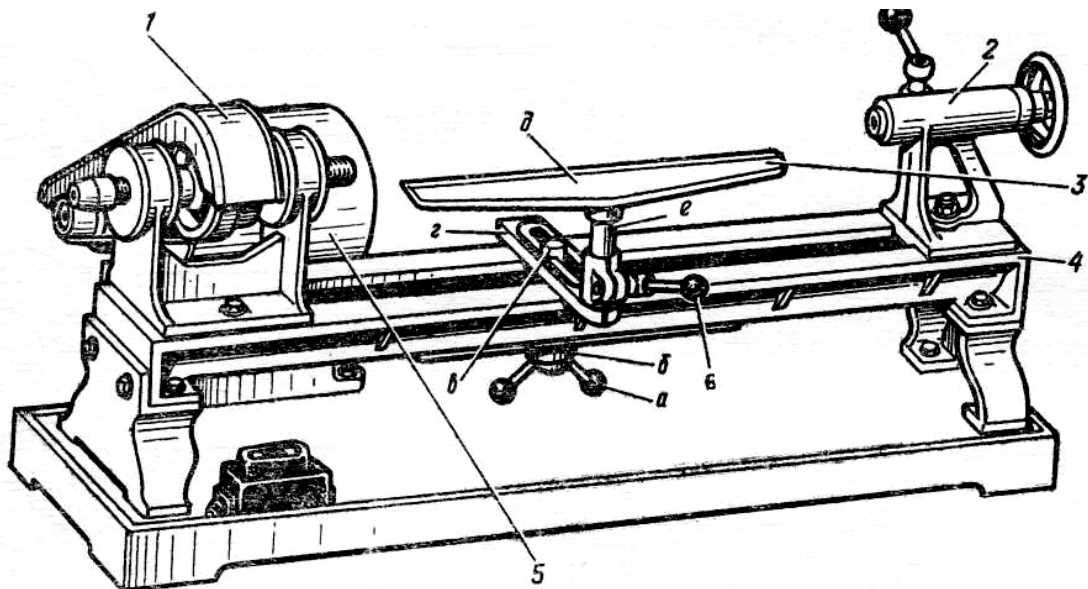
Токарний верстат для обробки деревини STD – 120:
